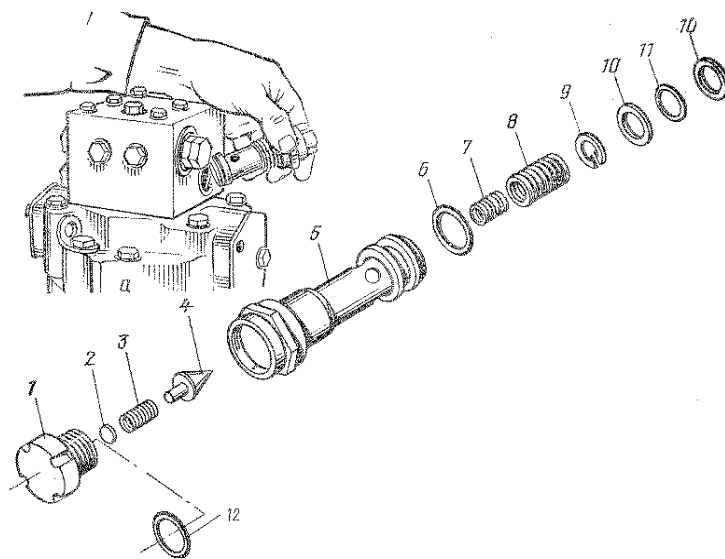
Клапан високого тиску: а – витягання клапана; б – деталі клапана; 1 – пробка; 2 – регулююча шайба; 3 та 7 – пружини; 4 – голка; 5 – корпус клапана; 6, 11 та 12 – кільця ущільнювачів; 8 – поршень; 9 – стопорне кільце; 10 – кільце.
